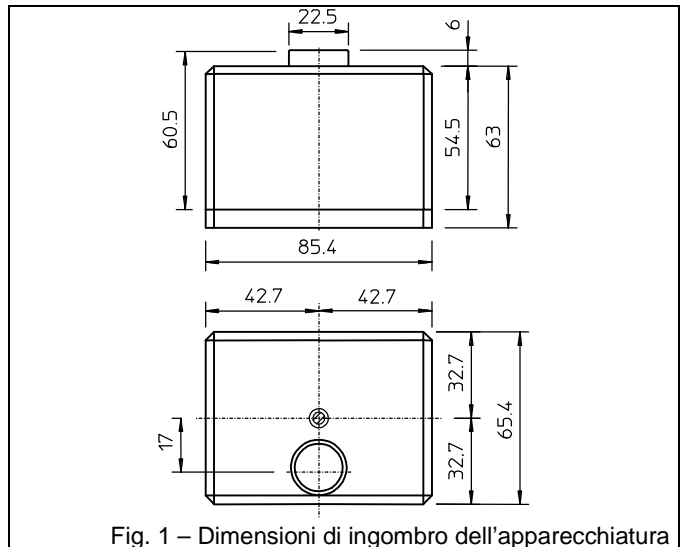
Dimensioni di ingombro dell'apparecchiatura
